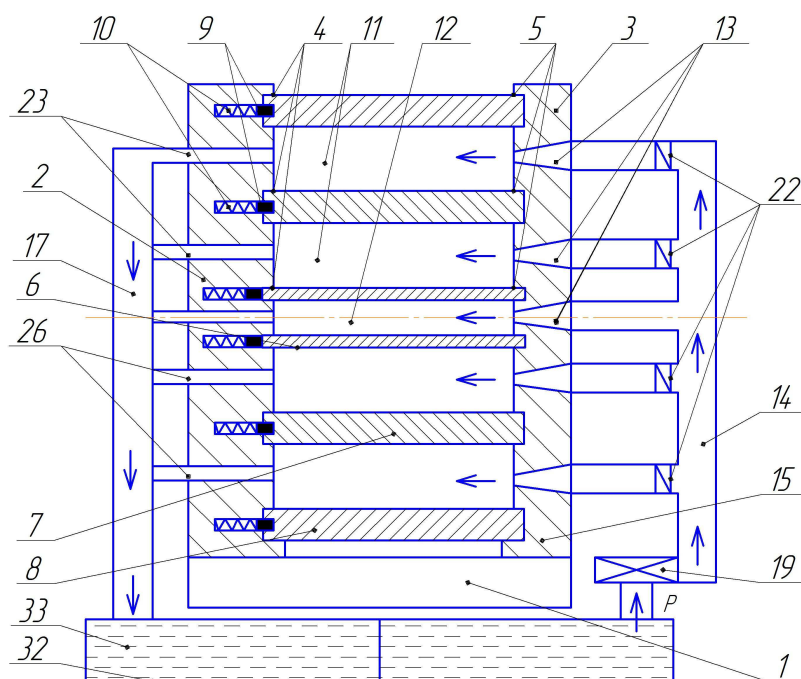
Продольное сечение устройства для гидроабразивной одновременной обработки внутренних и наружных поверхностей закрепленного пакета трубных заготовок
